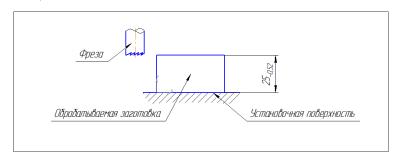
Пример обработки верхней плоскости заготовки
